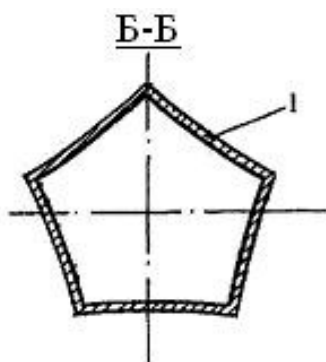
Сечение Б-Б корпуса 1 на рисунке 5 с центрами кривизны расположенными снаружи корпуса
